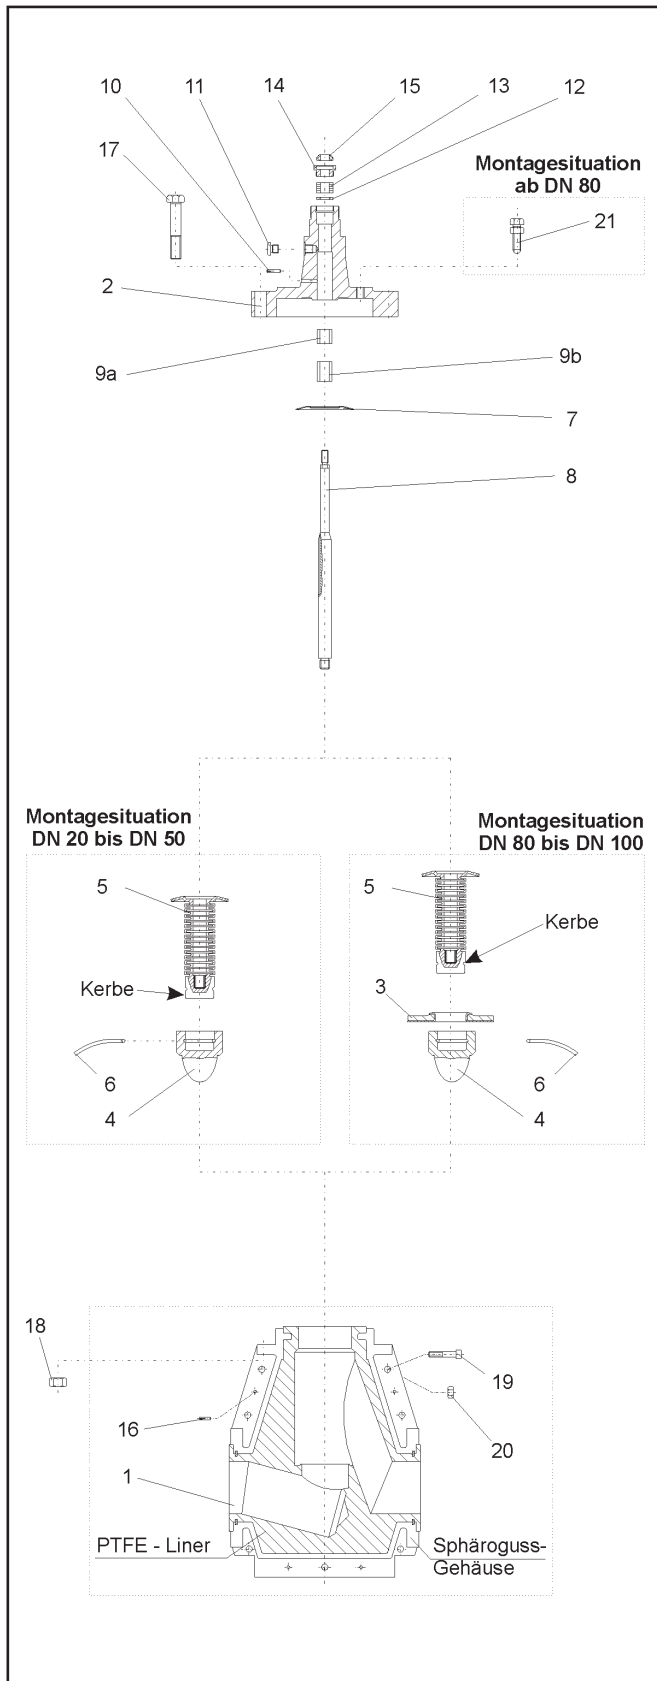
Explosionszeichnung des Stellventils BR 1z
